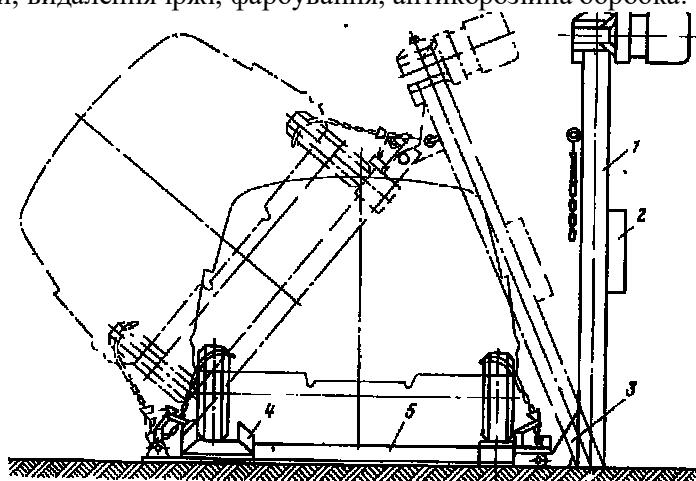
Електромеханічний перекидач П-129: 1 - стійка; 2 - затиск кріплення машини; 3 — каретка; 4 — підйомна рама; 5 — нерухома рама
